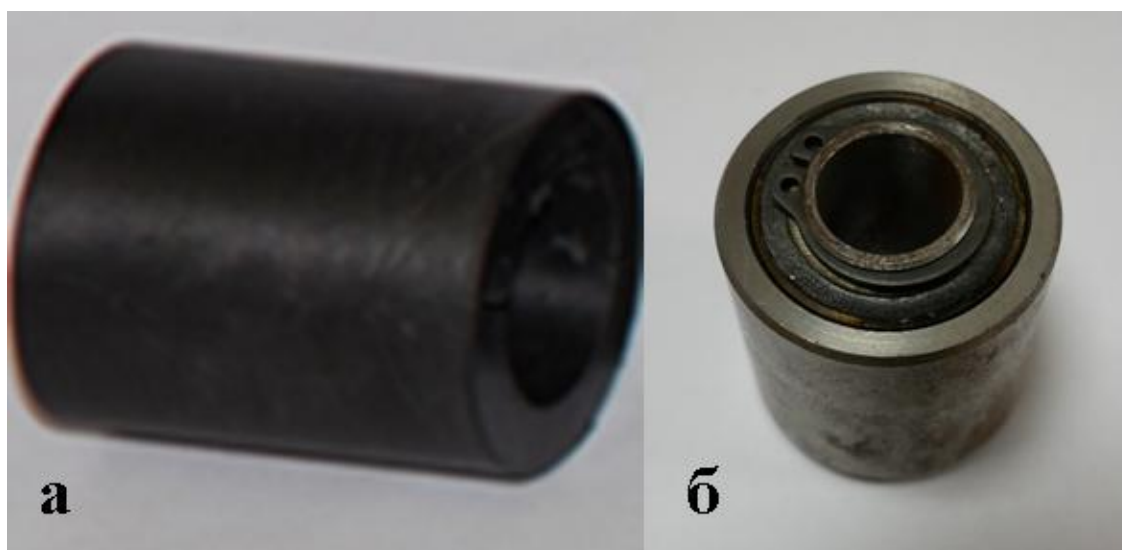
Експериментальний підшипник виготовлений з вуглецевої композиції.
